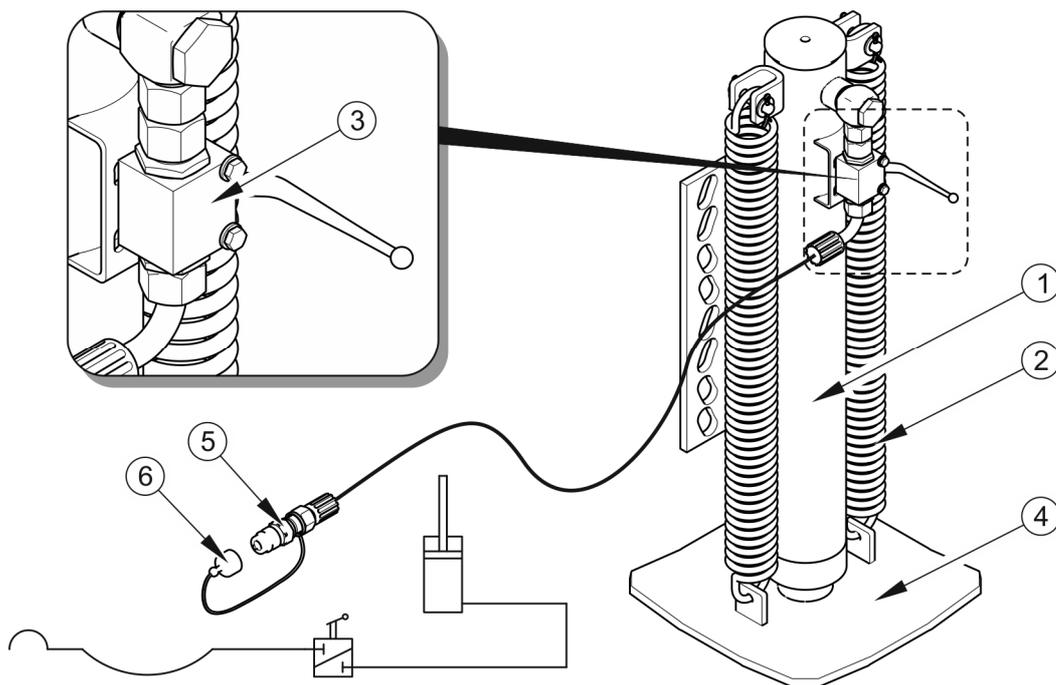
Costruzione e schema dell'impianto idraulico del supporto rettilineo
